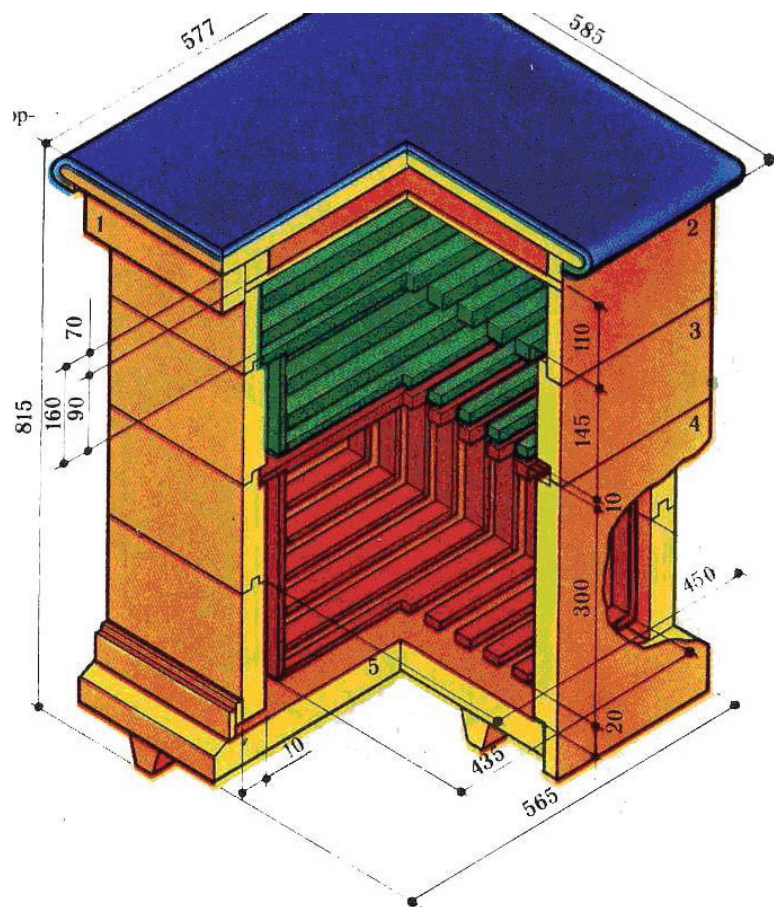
Типовой однокорпусный 12-рамочный улей с одним магазином:
